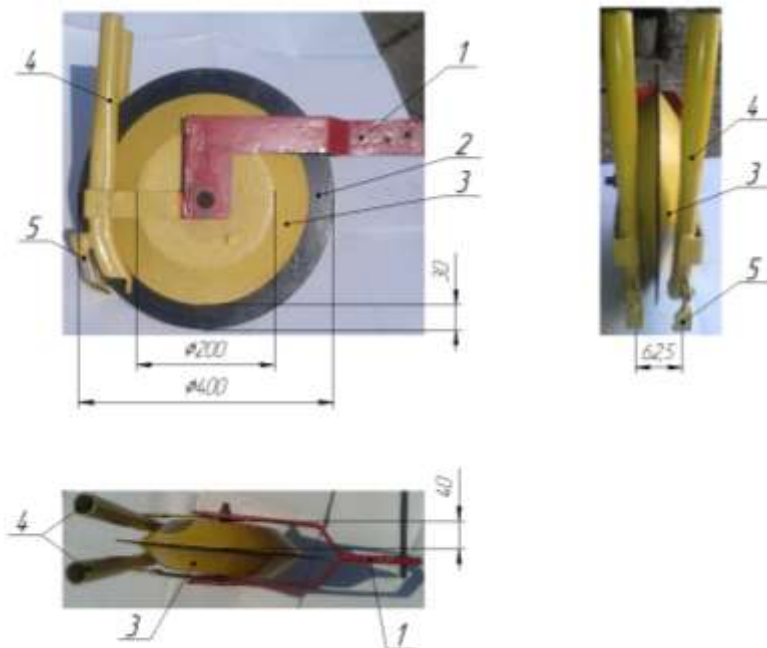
Новый макетный образец однодискового сошника с внешними симметричными ребрами-бороздкообразователями (вариант 1):
